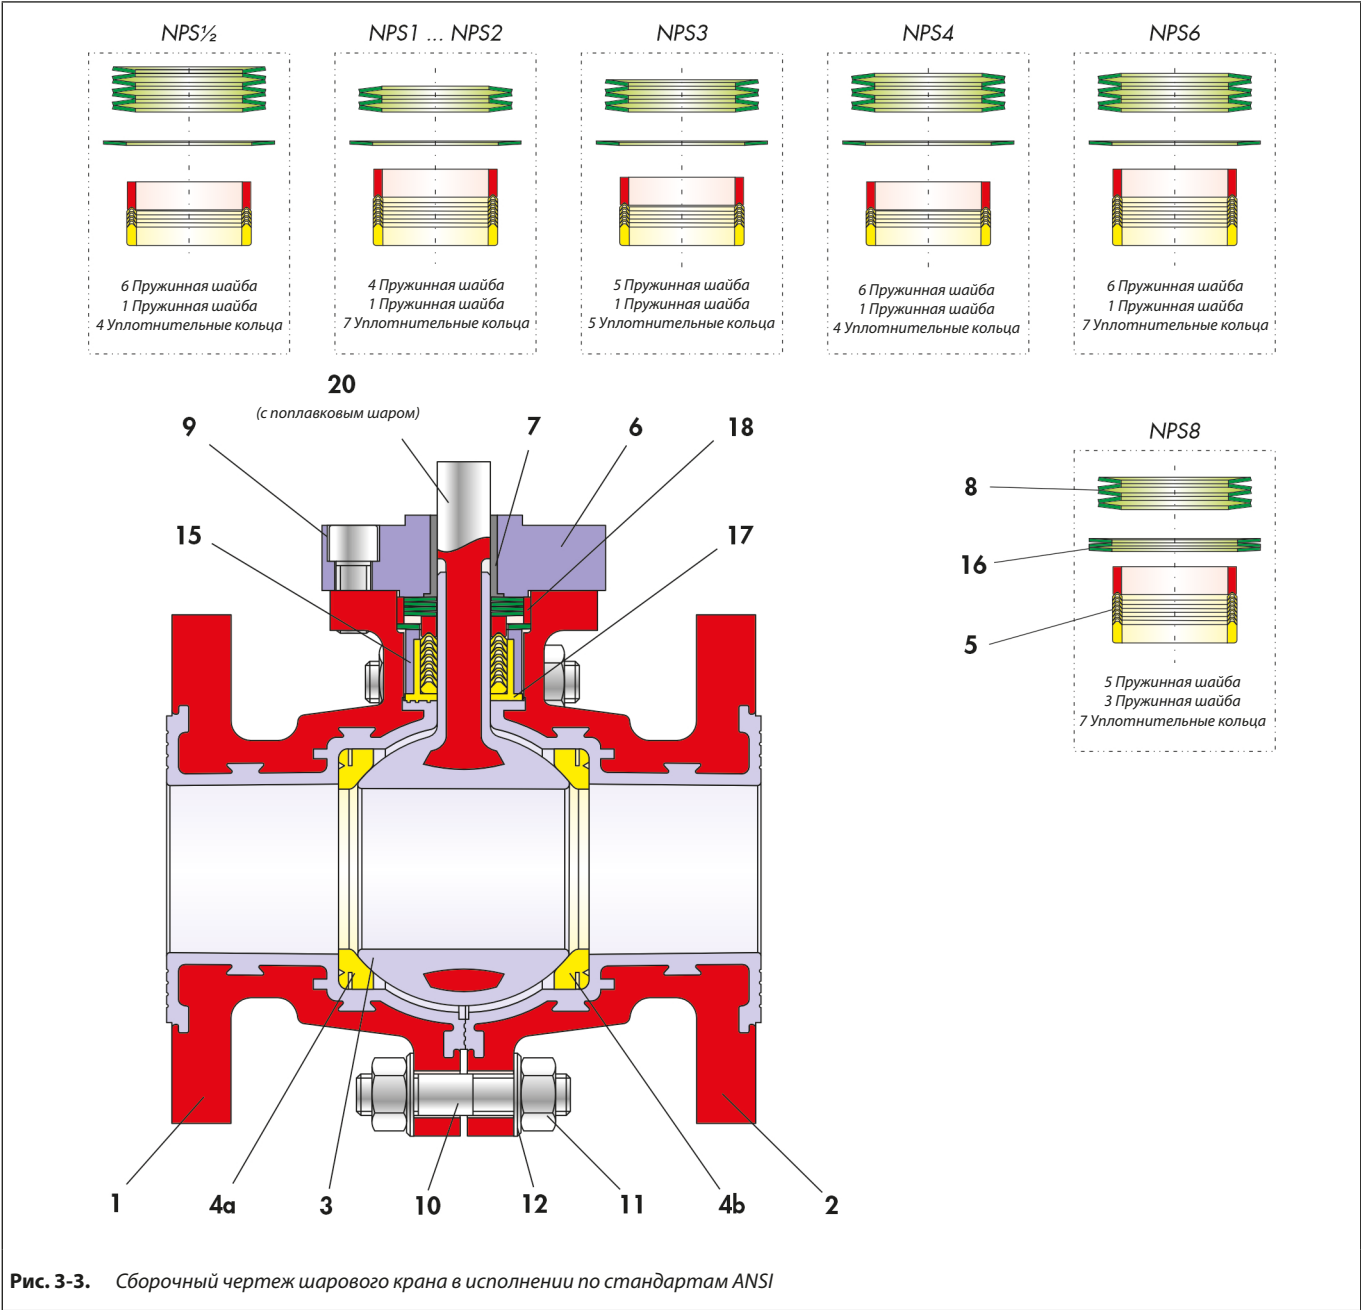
Сборочный чертеж шарового крана в исполнении по стандартам ANSI
